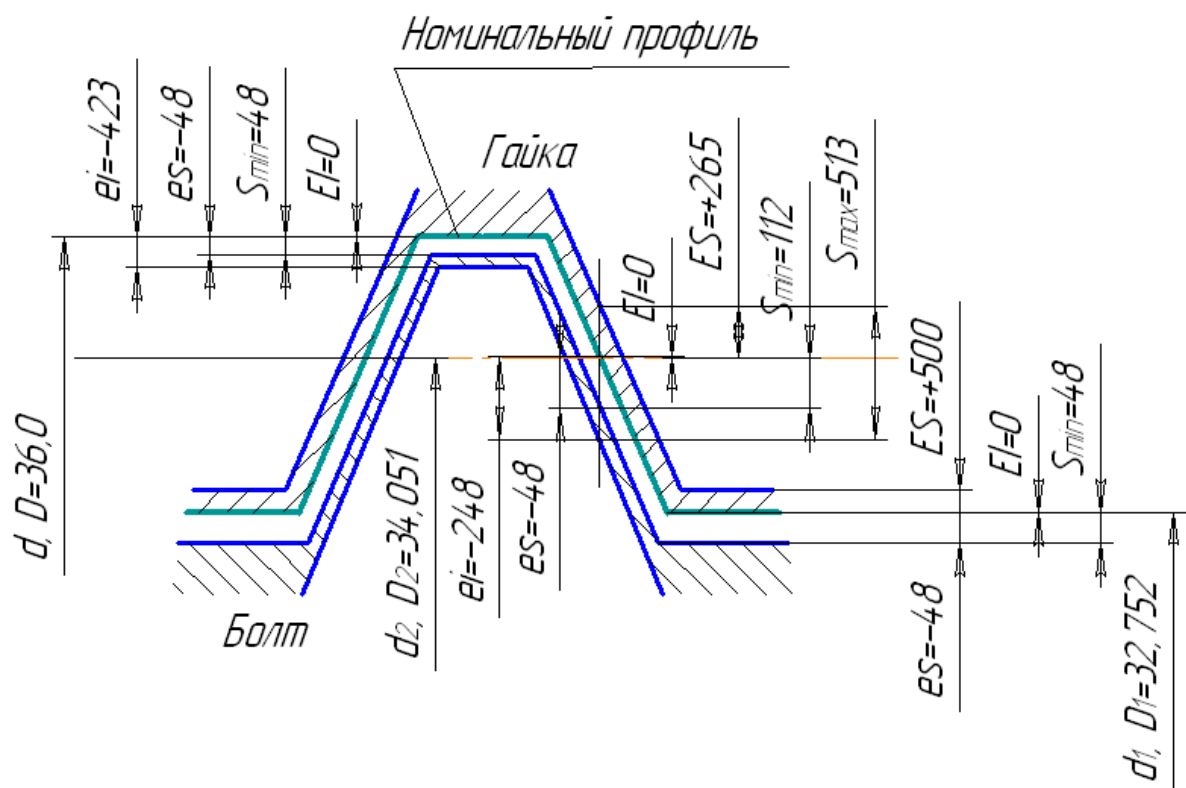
Схема полей допусков резьбового соединения $M36 \times 3-6H/6d$
